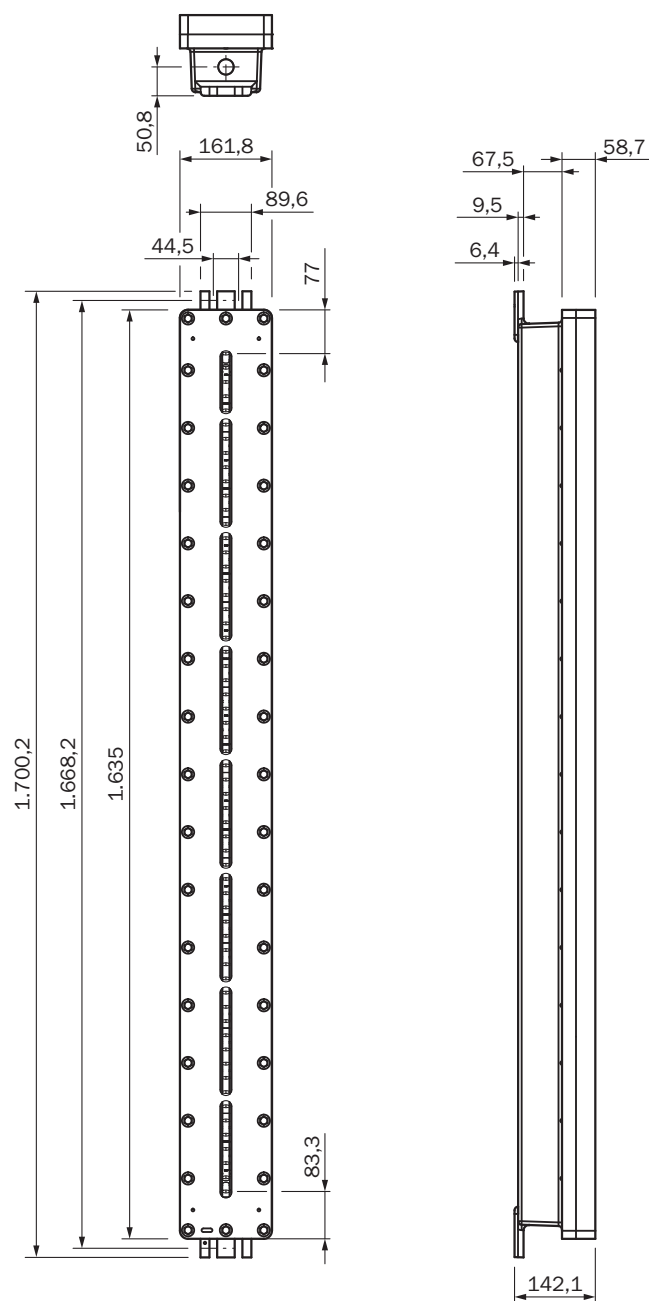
Desenho dimensional do emissor e do receptor, altura do campo de proteção 1500 mm
